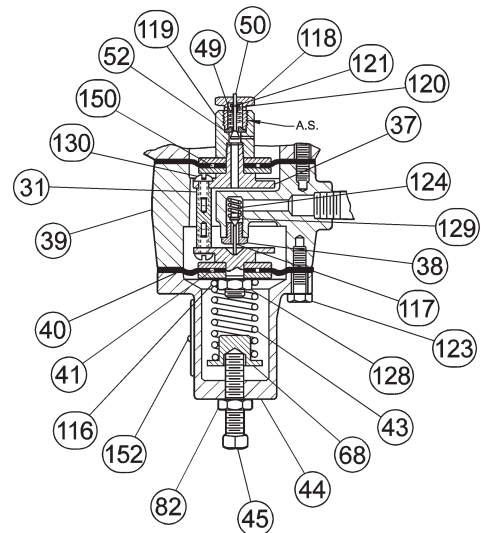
Extra Hochdruck-Steuerregler, Typ 61HP
